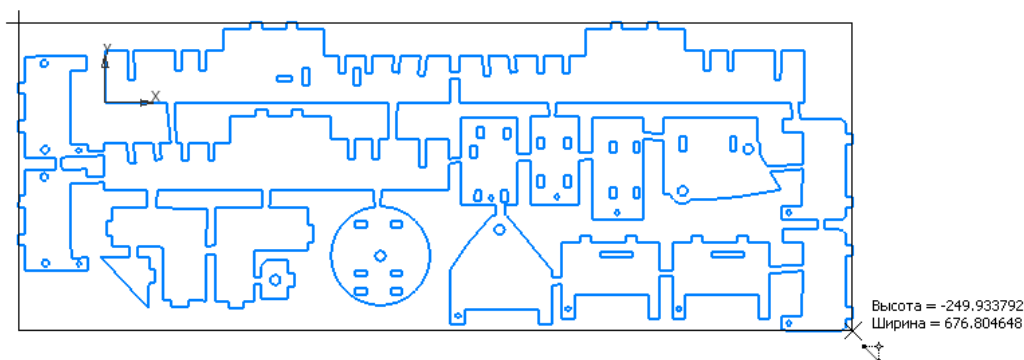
Эскиз деталей для изготовления стапеля для стального сварного кулака
